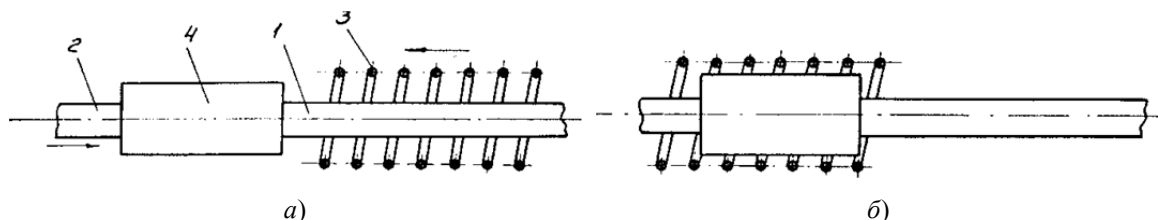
Схема скоростного нагрева заготовок перед штамповкой:
